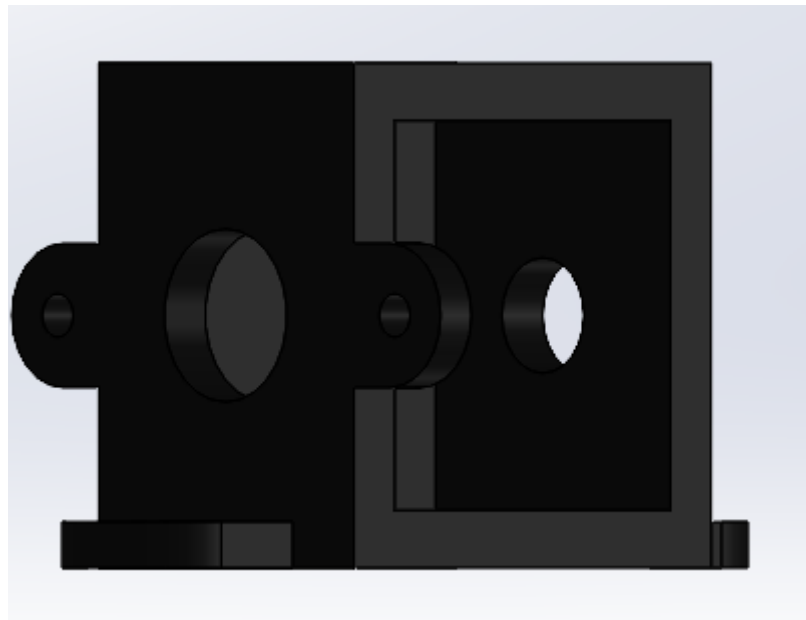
Ізометричний вид захисного кожуха для шківів
